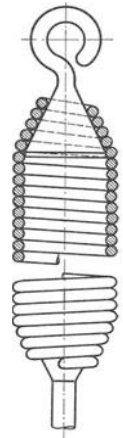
Zugfeder mit eingewickelten Ösenstücken.
